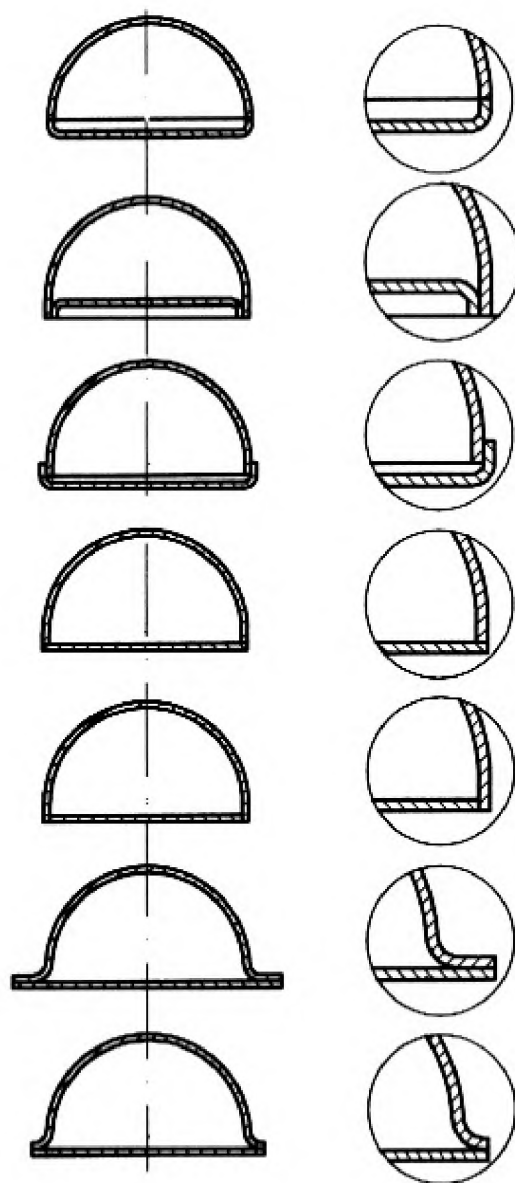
Варианты соединения стыков штампованных элементов оболочки перед сваркой
